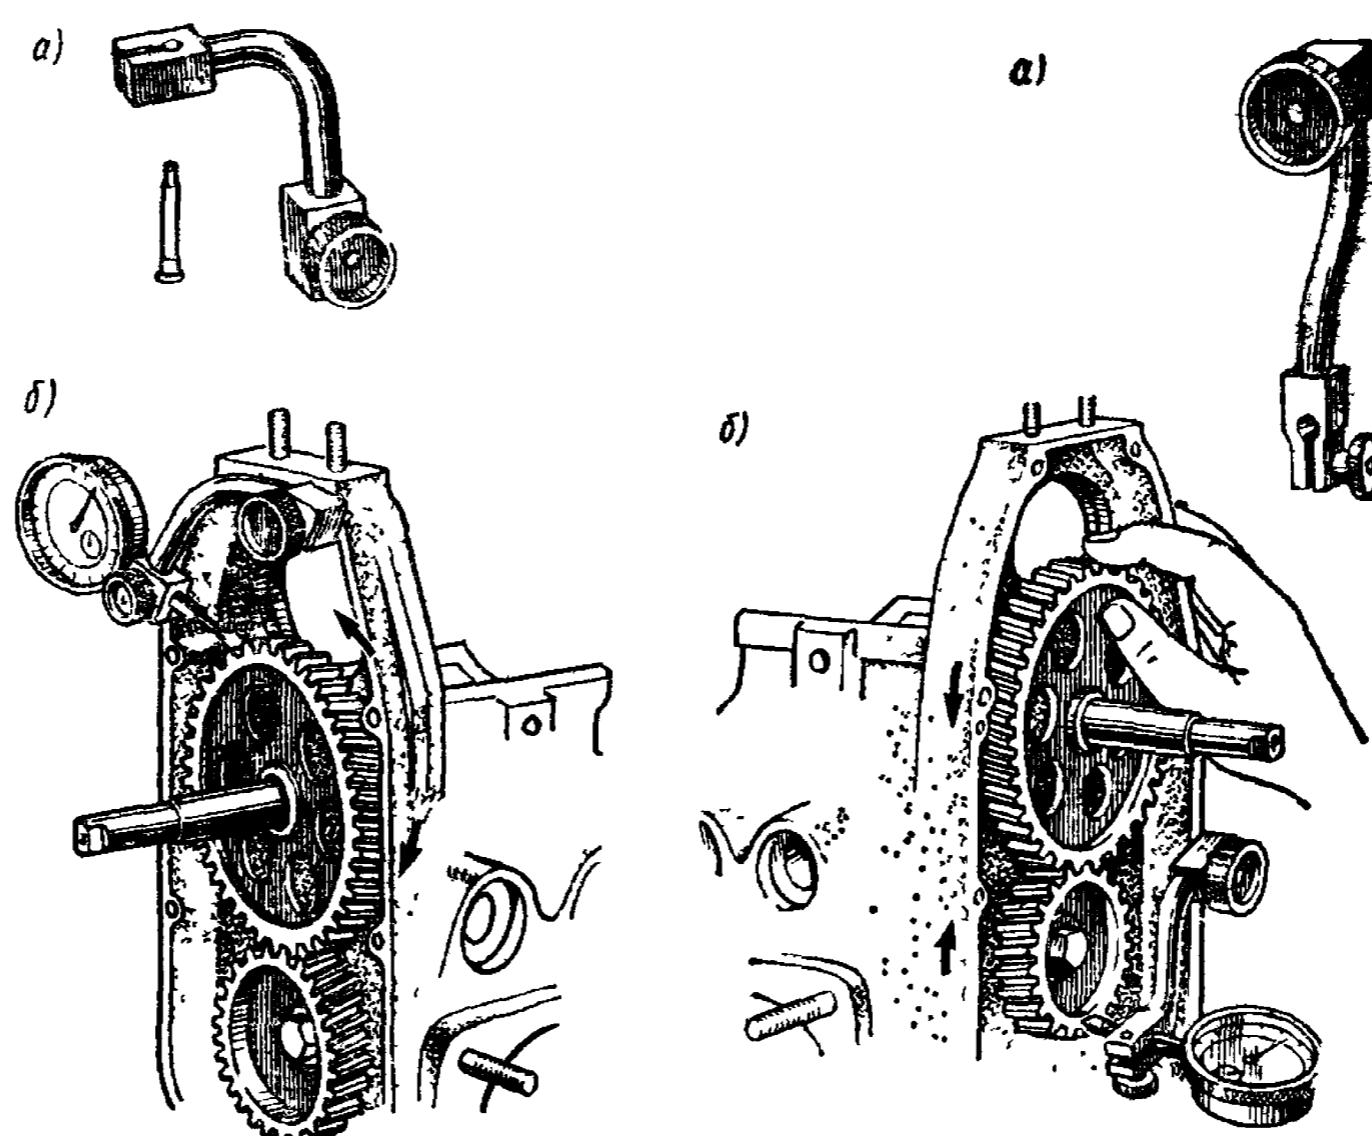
Замер бокового зазора в зацеплении зубчатых колес газораспределения: а — приспособление; б — установка приспособления на картере
